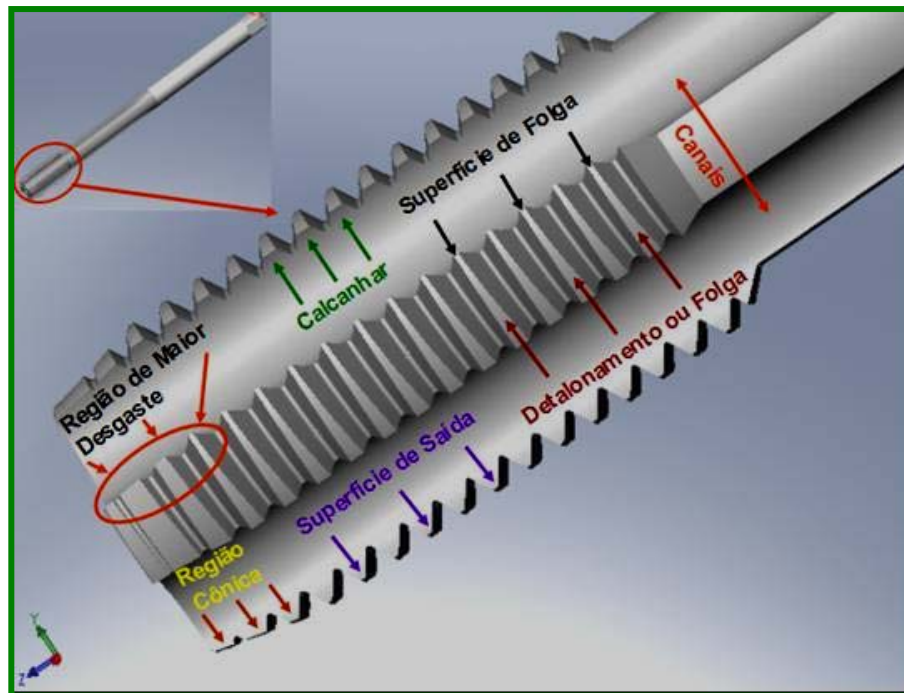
Geometria de um macho de corte utilizado na usinagem de roscas
